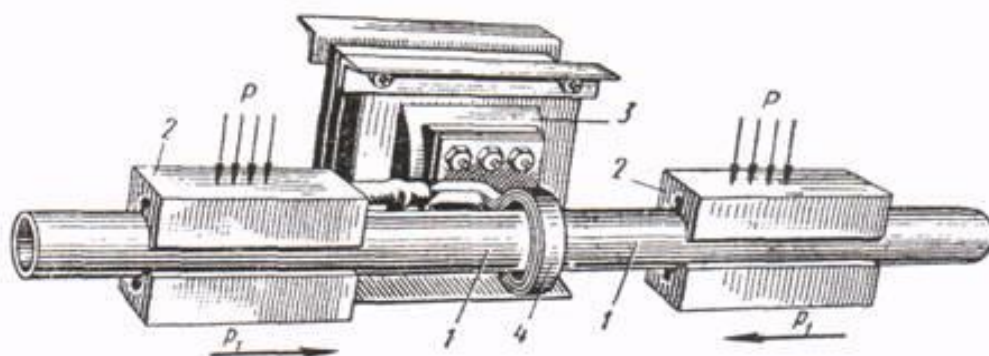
Схема индукционной стыковой сварки труб
